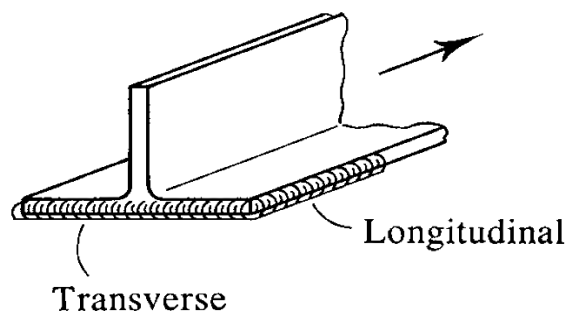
Soldadura longitudinal y soldadura transversal en un perfil de acero
